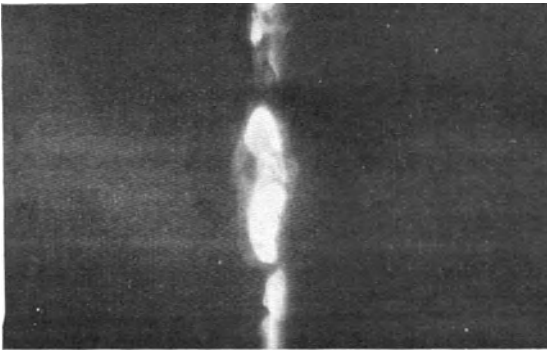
Röntgenaufnahme einer schlechten Schweißnaht.
